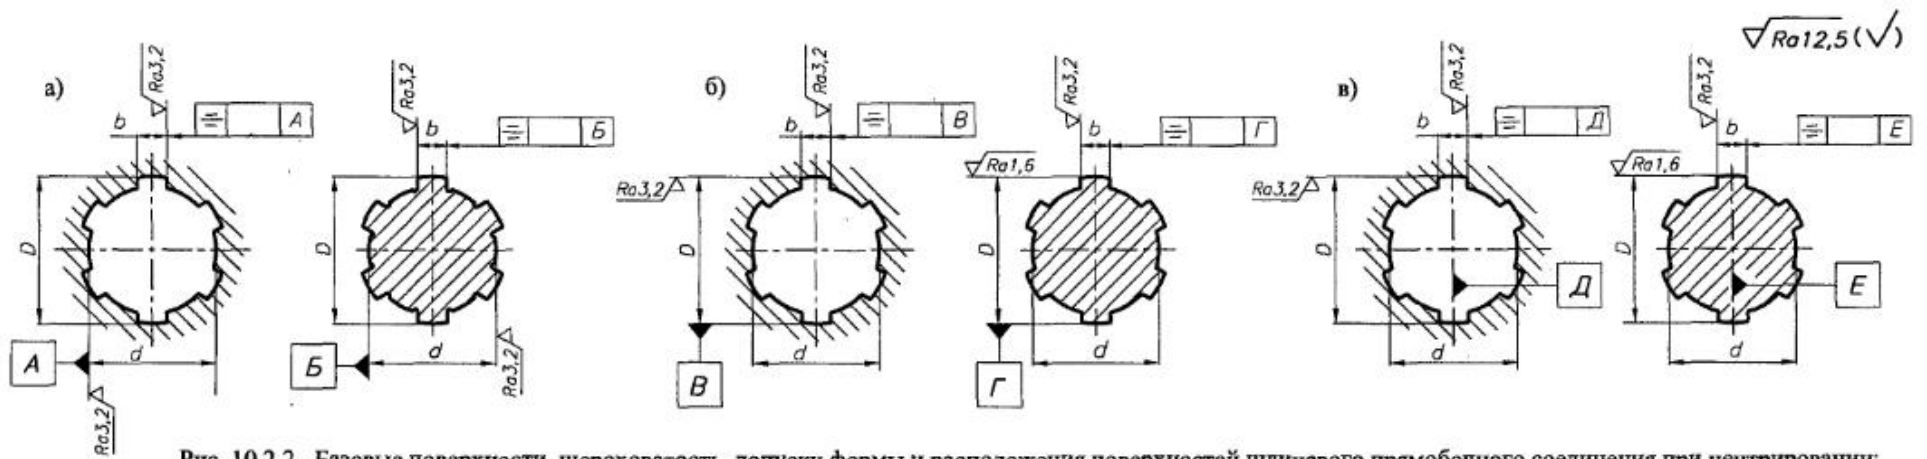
Базовые поверхности, шероховатость, допуски формы и расположения поверхностей шлицевого прямого соединения при центрировании: а) по d ; б) по D ; в) по b
